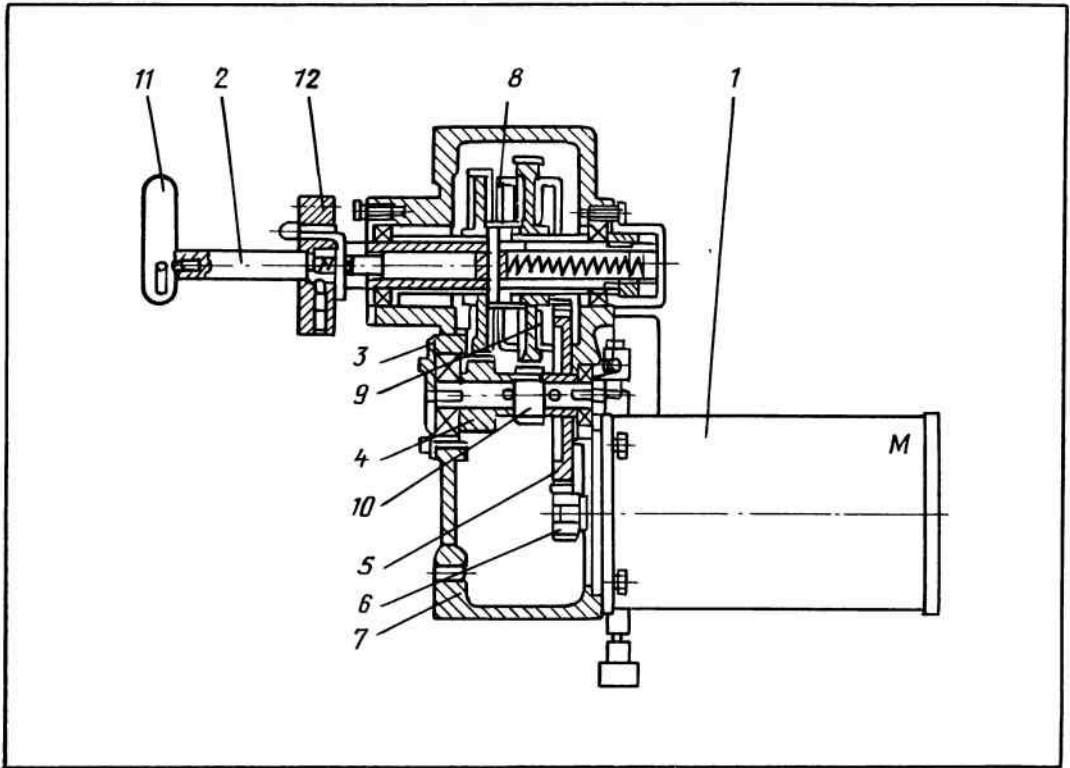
Конструкция намотывателя кинопроектора 35КСА (модель «Мир-5»): 1 — электродвигатель; 2 — вал; 3, 4, 5, 6, 9 — зубчатые колеса; 7 — корпус редуктора; 8 — механизм переключения скорости; 10 — вал-шестерня; 11 — защелка
